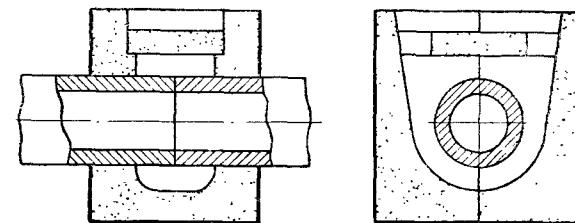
Сварочные формы для толстостенных труб.
